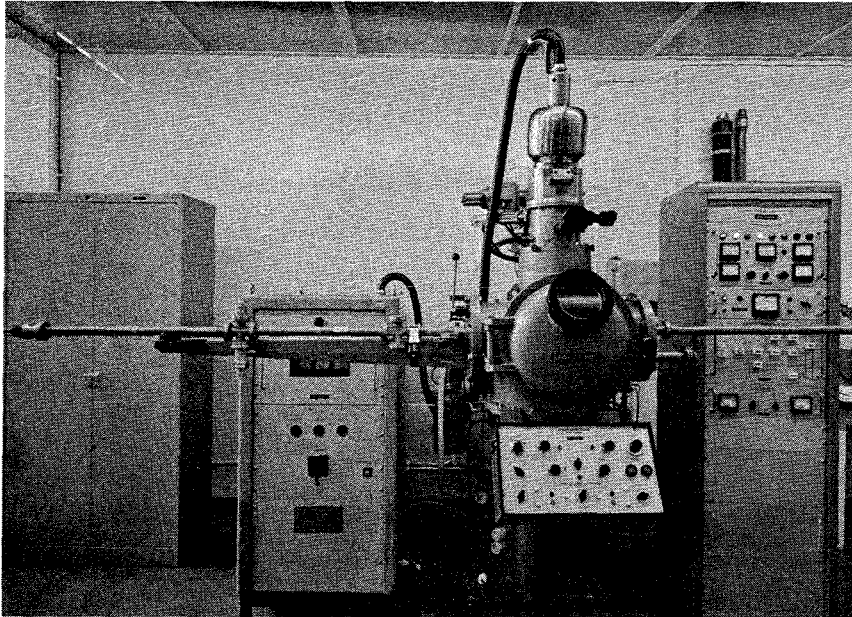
Elektronenstrahl-Schweißanlage ESW5
